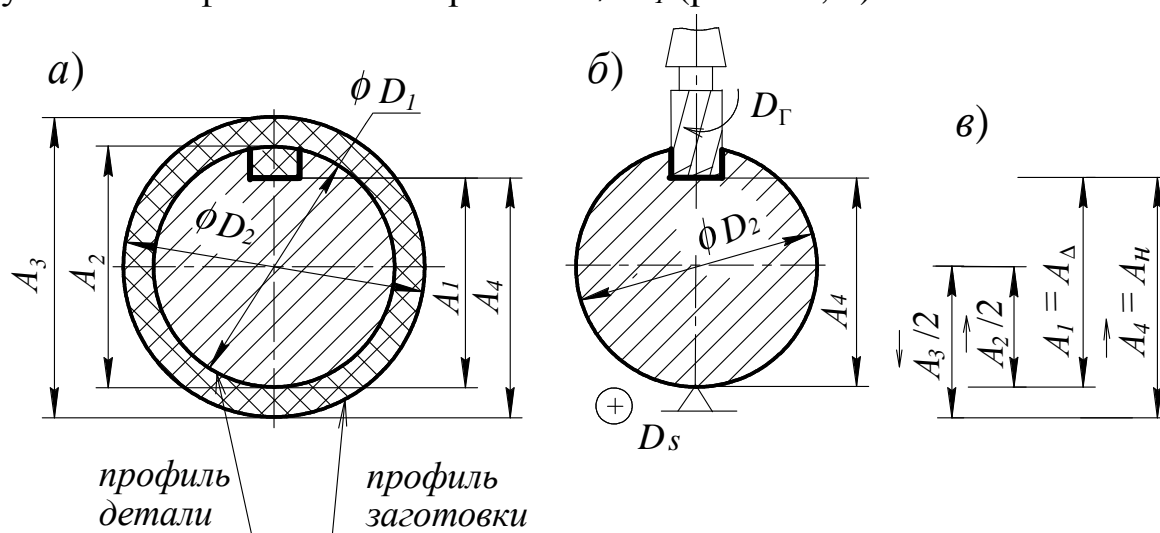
Схема изготовления шпоночного паза на валике (а), операционный эскиз фрезерования паза (б) и размерная цепь для определения операционного размера (в)
